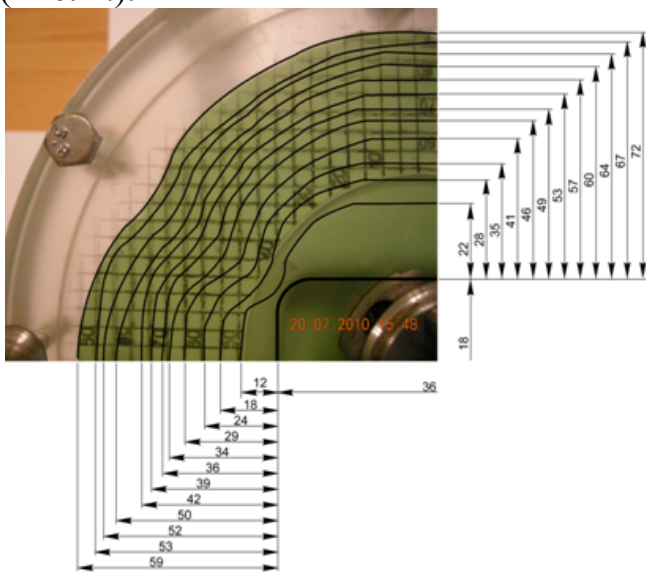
Результати “зворотнього” витягування при різній глибині умовної коробчатої деталі прямокутної форми з розмірами у плані 72x36 мм.
